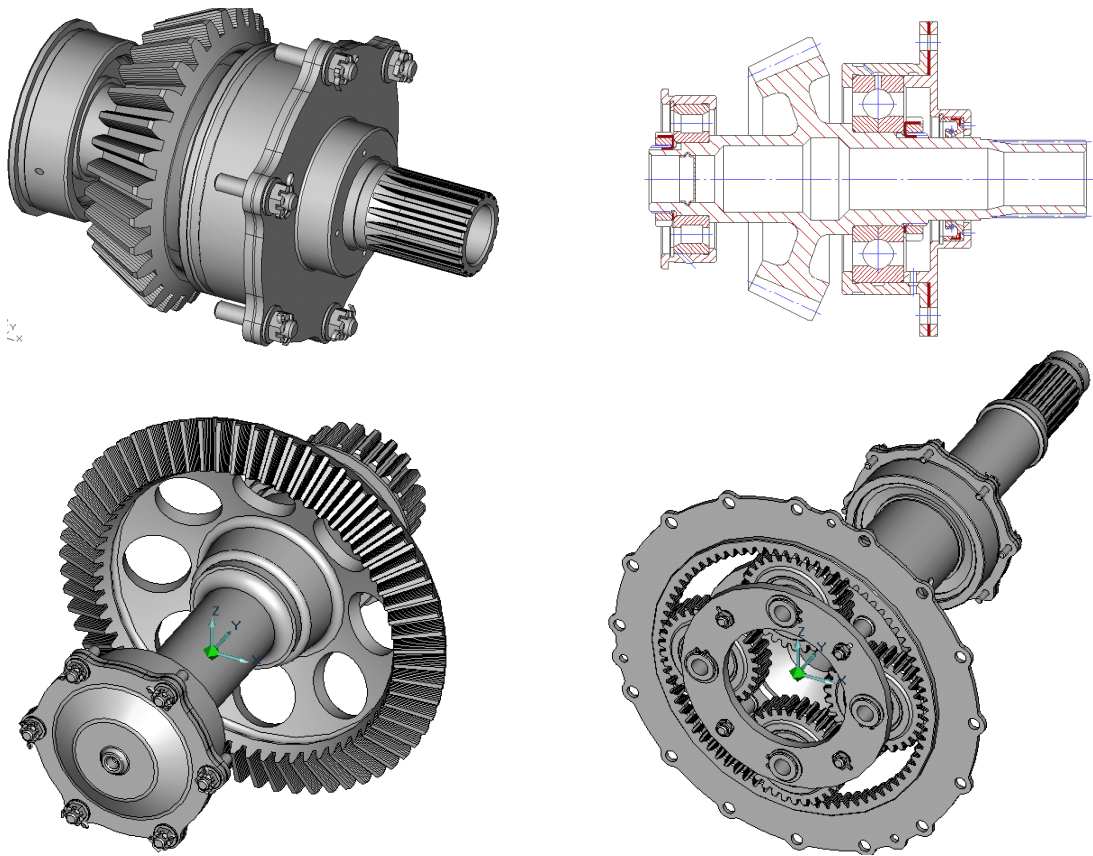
3D и 2D модели входного (вверху) и 3D модели промежуточного и выходного валов с планетарной передачей редуктора
